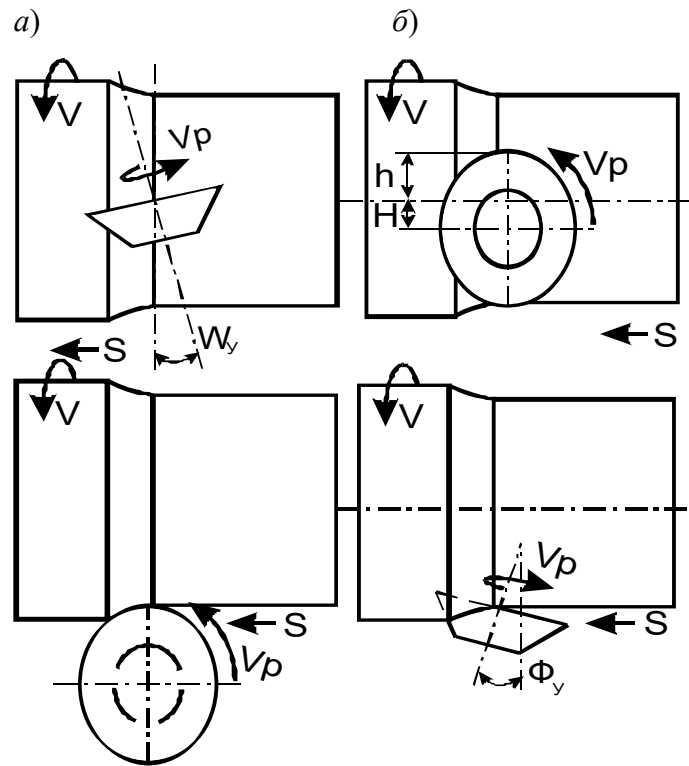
Схема расположения координатных плоскостей и углов режущего элемента чашечного резца
